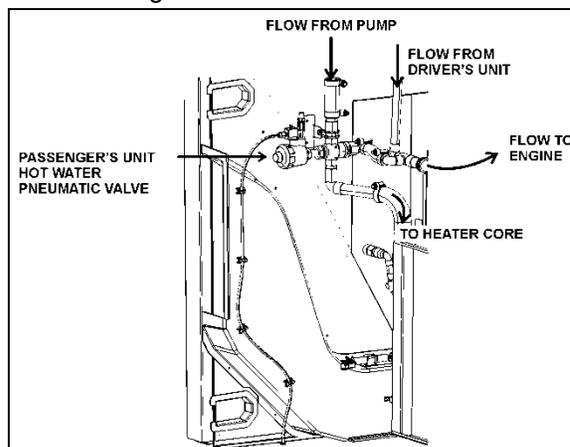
ENSAMBLE DE VÁLVULA NEUMÁTICA DE AGUA CALIENTE DE UNIDAD DE PASAJEROS 22240
